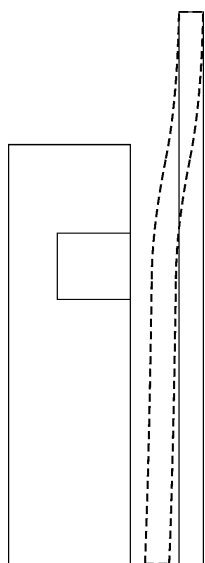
Деформований стан індуктора та заготовки. Суцільна лінія – початковий стан, штрихова лінія – деформований стан
